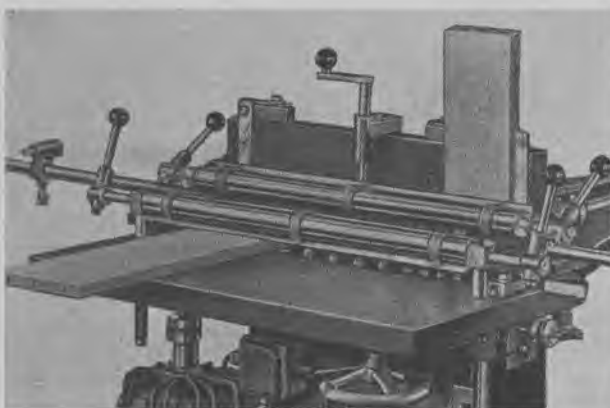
Dyvelboremaskine med ca. 20 spindler.
